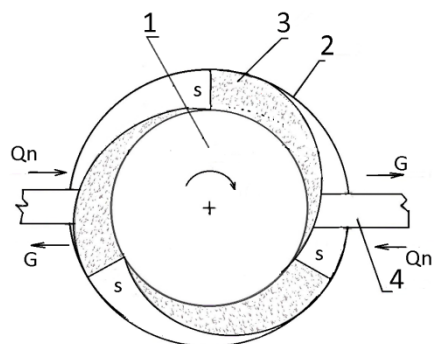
Схема трехкамерного ЗГД лопастного типа: 1-ротор; 2-статор; 3-лопатки; 4-пластина.
